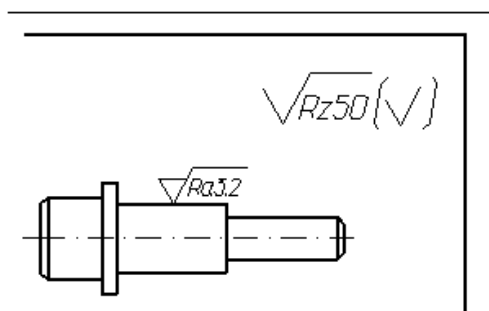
Указание шероховатости одинаковой для части поверхностей изделия
